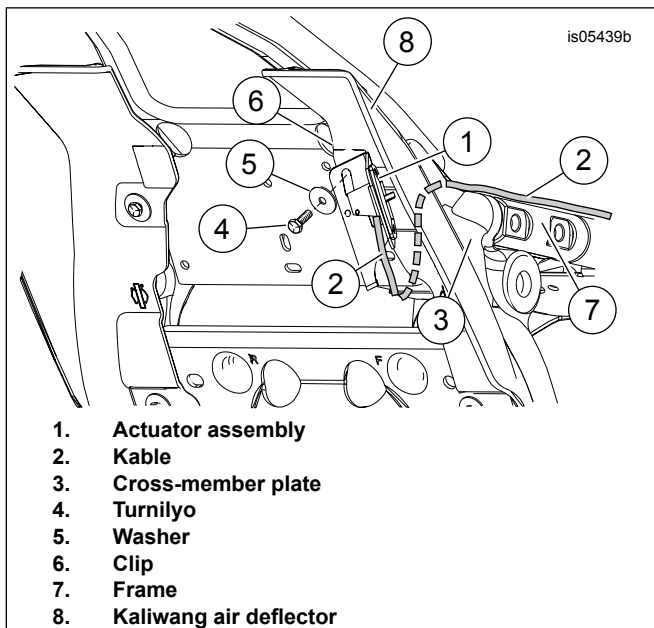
Pagkakabit ng Actuator Assembly na may Mid-Frame Air Deflector
